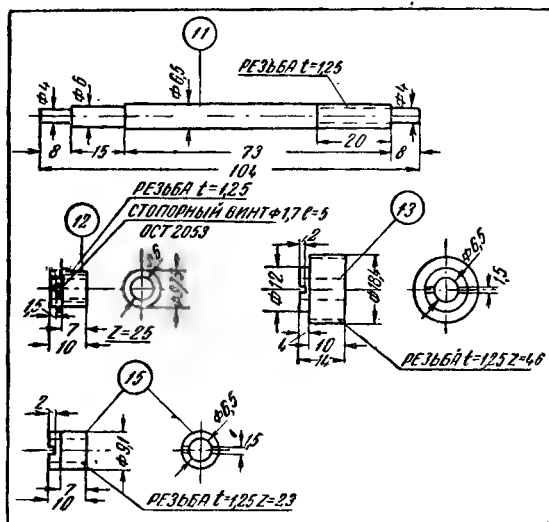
Детали механизма смещения: 11—промежуточный винт, 12 и 13—шестерни
